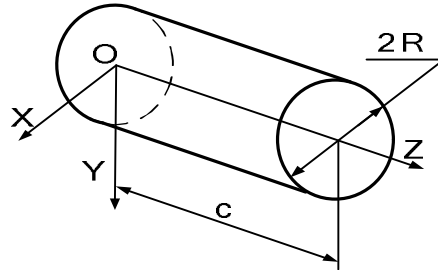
Цилиндрическая и торцевая поверхность, обрабатываемая на станке
